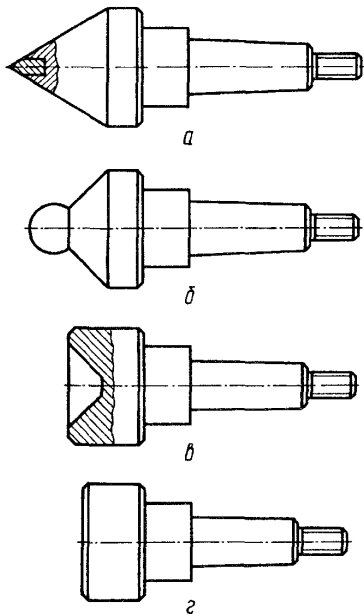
Змінні вставки в обертовий центр: а - з твердосплавним кінцем на робочому конусі; б - з кульковим кінцем; в - зі зворотним конусом; г - з тертьовим притискуванням
